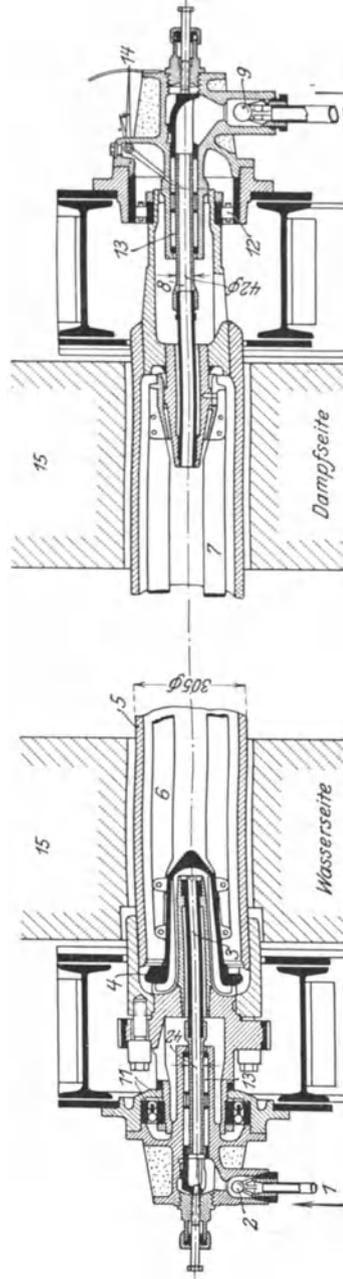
Rotor des Atmos-Kessels der Studenburger Maschinenaabrik in waagerechter Ausrichtung. 1 = Speisewassereintritt, 2 = Rückschlagventil (sperrt den Rotor bei einer größeren Undichtheit selbsttätig vom Dampfnetz ab), 3 = Zufuhr des Speisewassers in den Rotor, 4 = Zentrifugier- und Verteilkörper, 5 = Rohr des Rotors, 6 = Mitnehmer-schaukel, 7 = 6, 8 = Abfuhr des Dampfes, 9 = 2, 10 = zum Überhitzer, 11 = Kugellager (festes Lager), 12 = Rollenlager (verschiebbares Lager), 13 = Stöpseltische, 14 = Ausdehnungsanzeiger für Rotorrohr, 15 = Kesseleinmauerung. Beachte: Vermeiden von Teilen von großem Durchmesser. "Wasserumlauf" fehlt. Statt seiner wird Wasserring von 30 bis 50 mm Dicke durch Zentrifugalkraft an Rotorrohr angepreßt.
